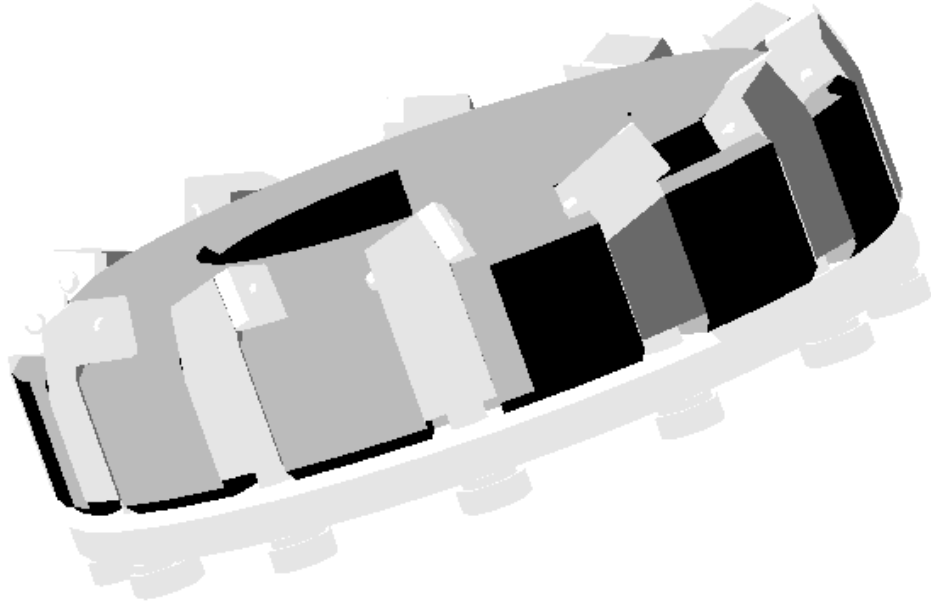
Конструкція збірної торцевої фрези (ГОСТ 22085-76 )
